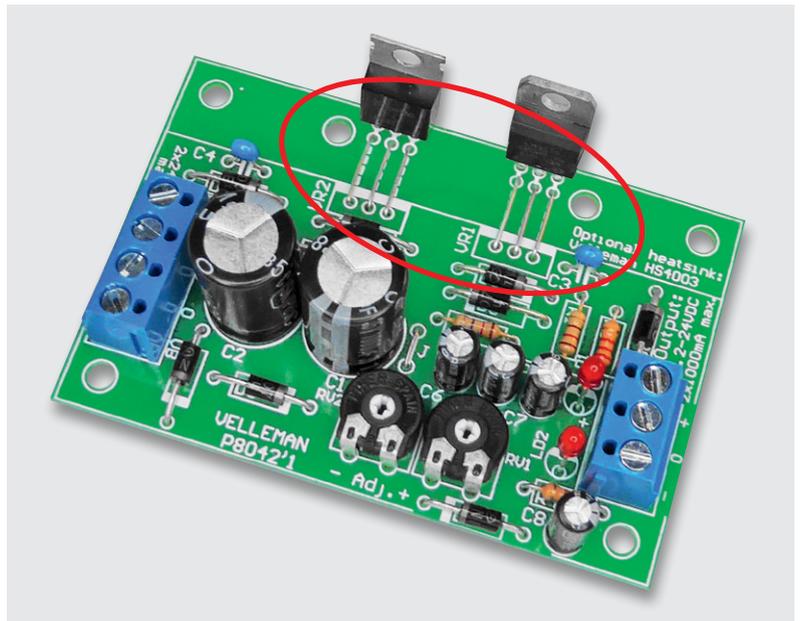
Die Bestückung der Spannungsregler und der Drahtbrücken für die Montage an einer Gehäusewand
